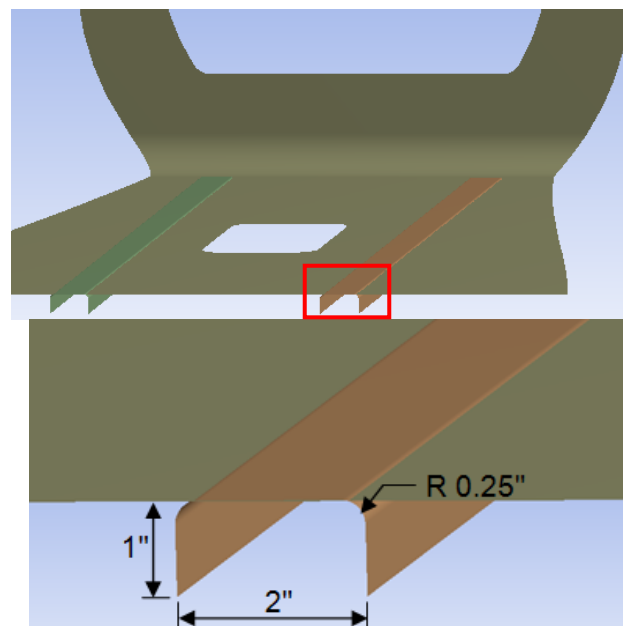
Emplacement des raidisseurs du plancher (gauche) et dimensions (droite)
